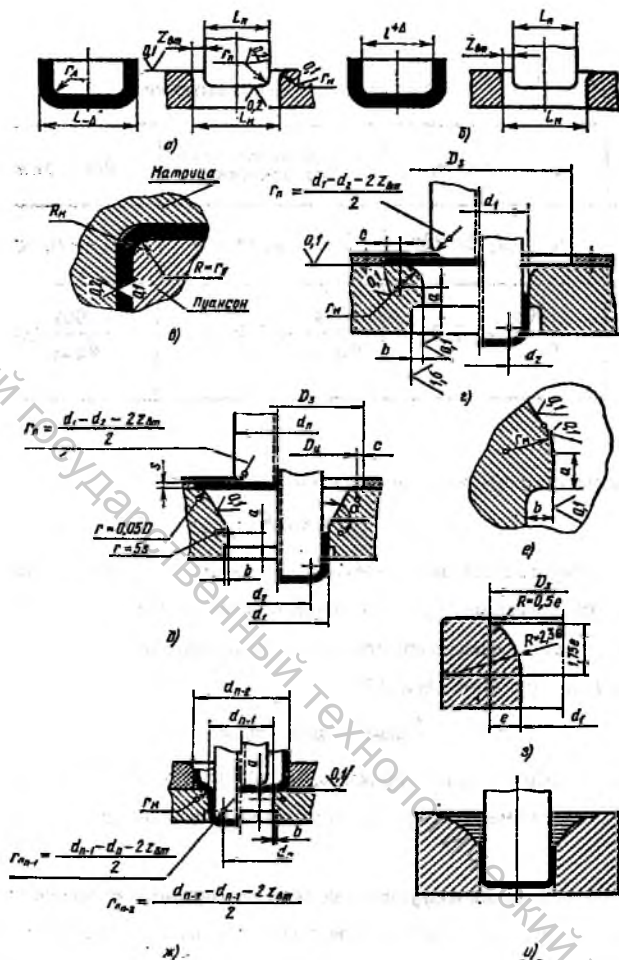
Исполнительные размеры и конструктивное исполнение рабочих элементов штампа [3]:
